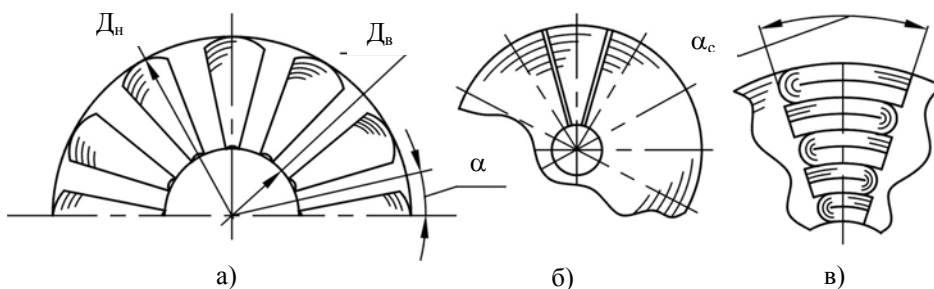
Аксиальный стыковой магнитопровод (а) со стержнями из витой разрезной заготовки (б) или коаксиальных разрезных опрессованных элементов (в)
